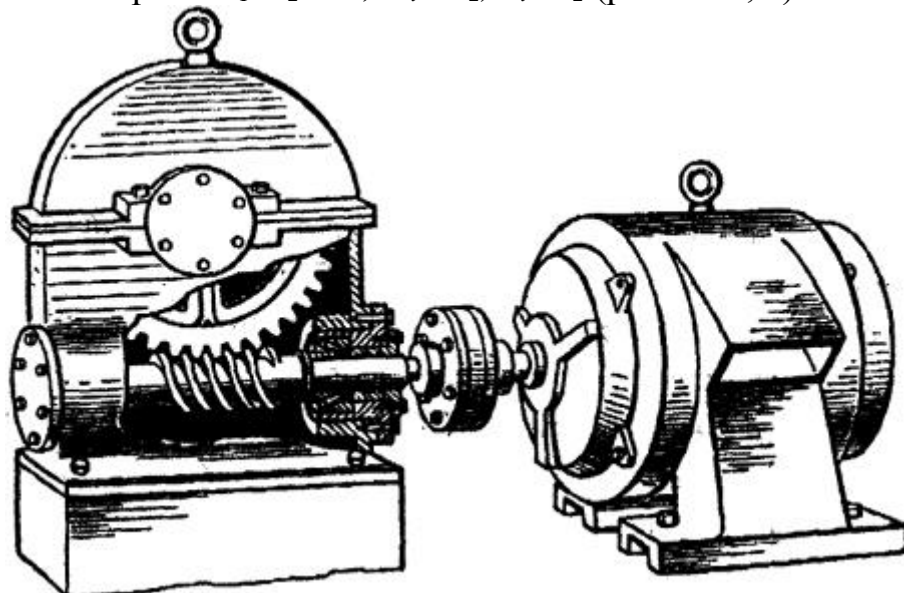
Привод "Электродвигатель - червячный редуктор"
